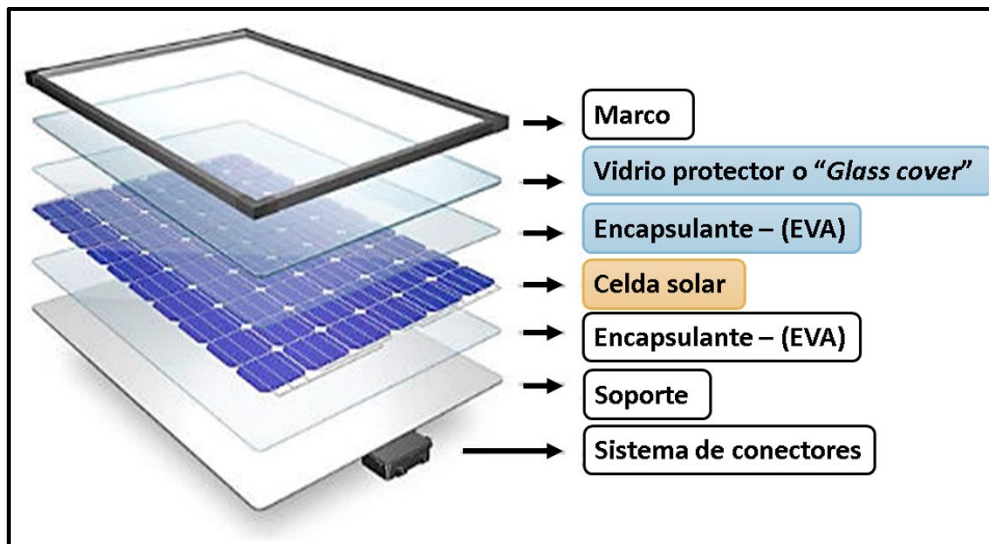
Componentes de un panel solar comercial, adaptado de [59].
